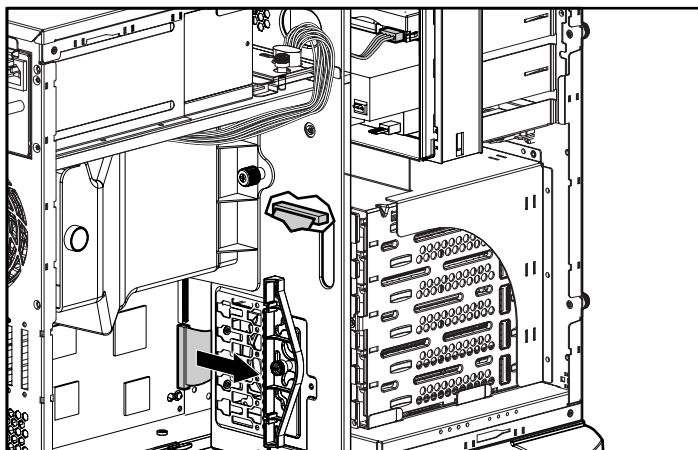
Remoção do cabo SCSI do conector SCSI principal
